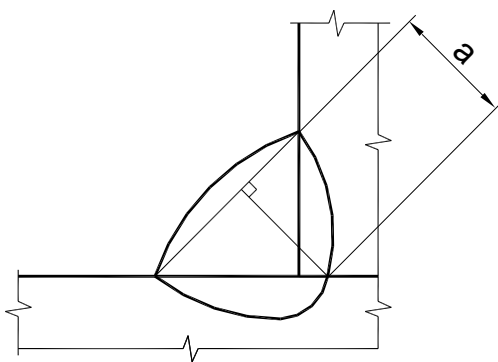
Толщина углового сварного шва с полным проваром
